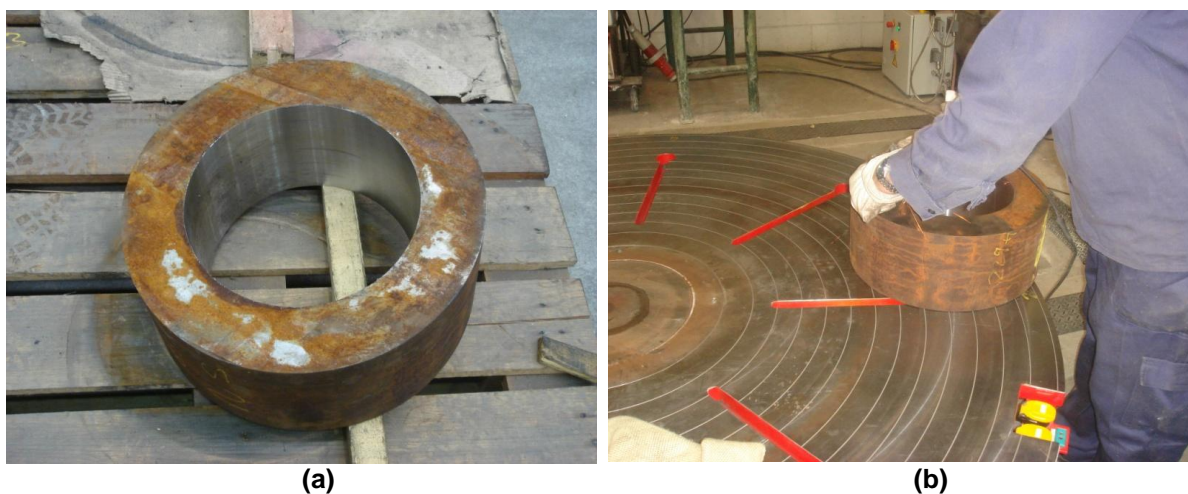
(a) peça a ser soldada com detalhe da região interna usinada visando remoção de camada oxidada e (b) Detalhes de montagem da amostra em dispositivo para execução da soldagem TIG.
